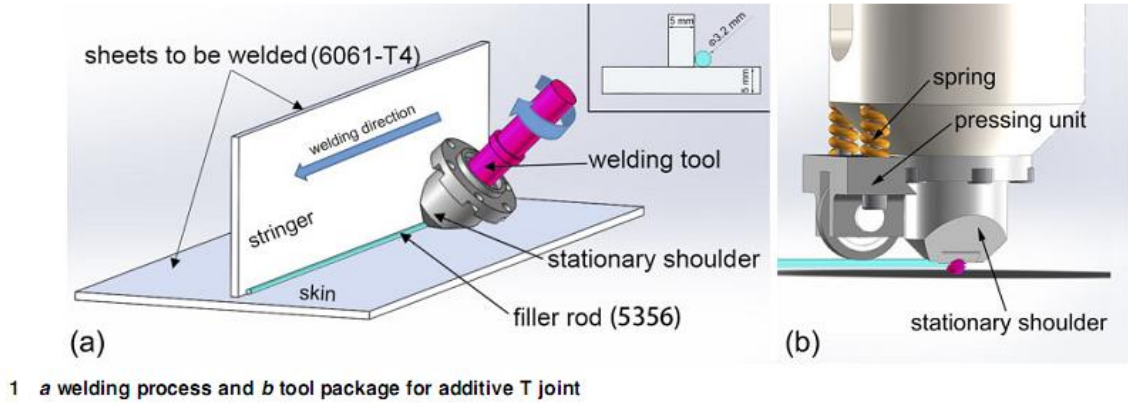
FSW con hombro estacionario, para soldaduras con una disposición en T con y sin adición de material [39].
